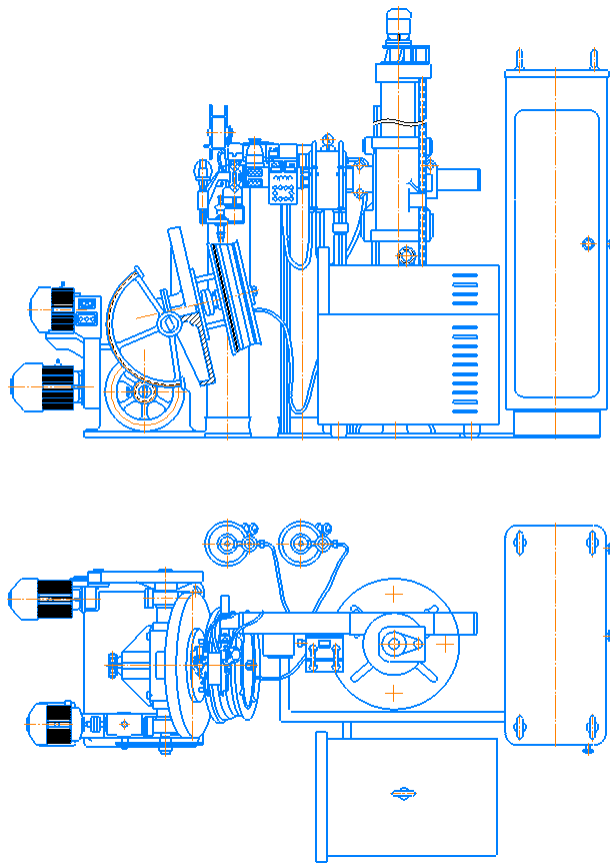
Стенд для сборки и сварки кольцевых швов
